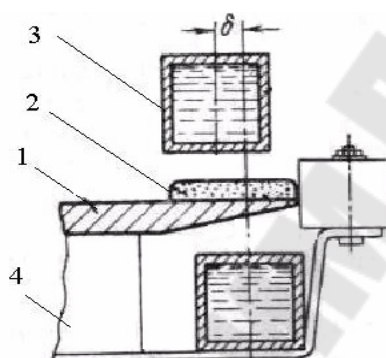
Схема расположения наплавляемой детали в индукторе:
